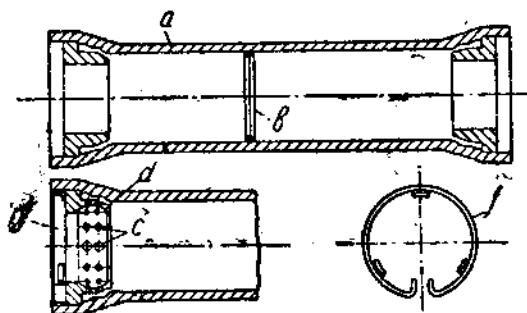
Кокиль для одновременной отливки двух раstrубных труб.
